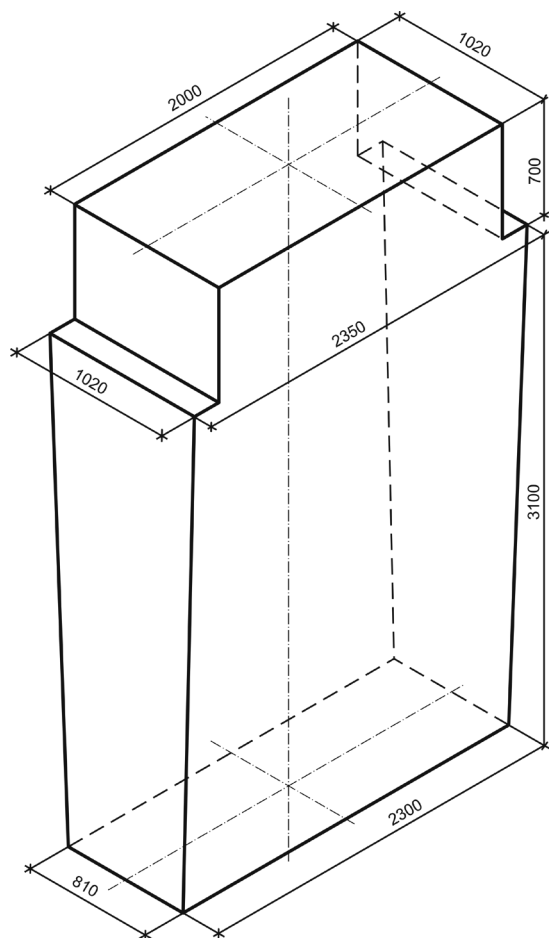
Геометрические размеры внутренней полости изложницы и прибыльной надставки для отливки 50-тонного листового слитка
